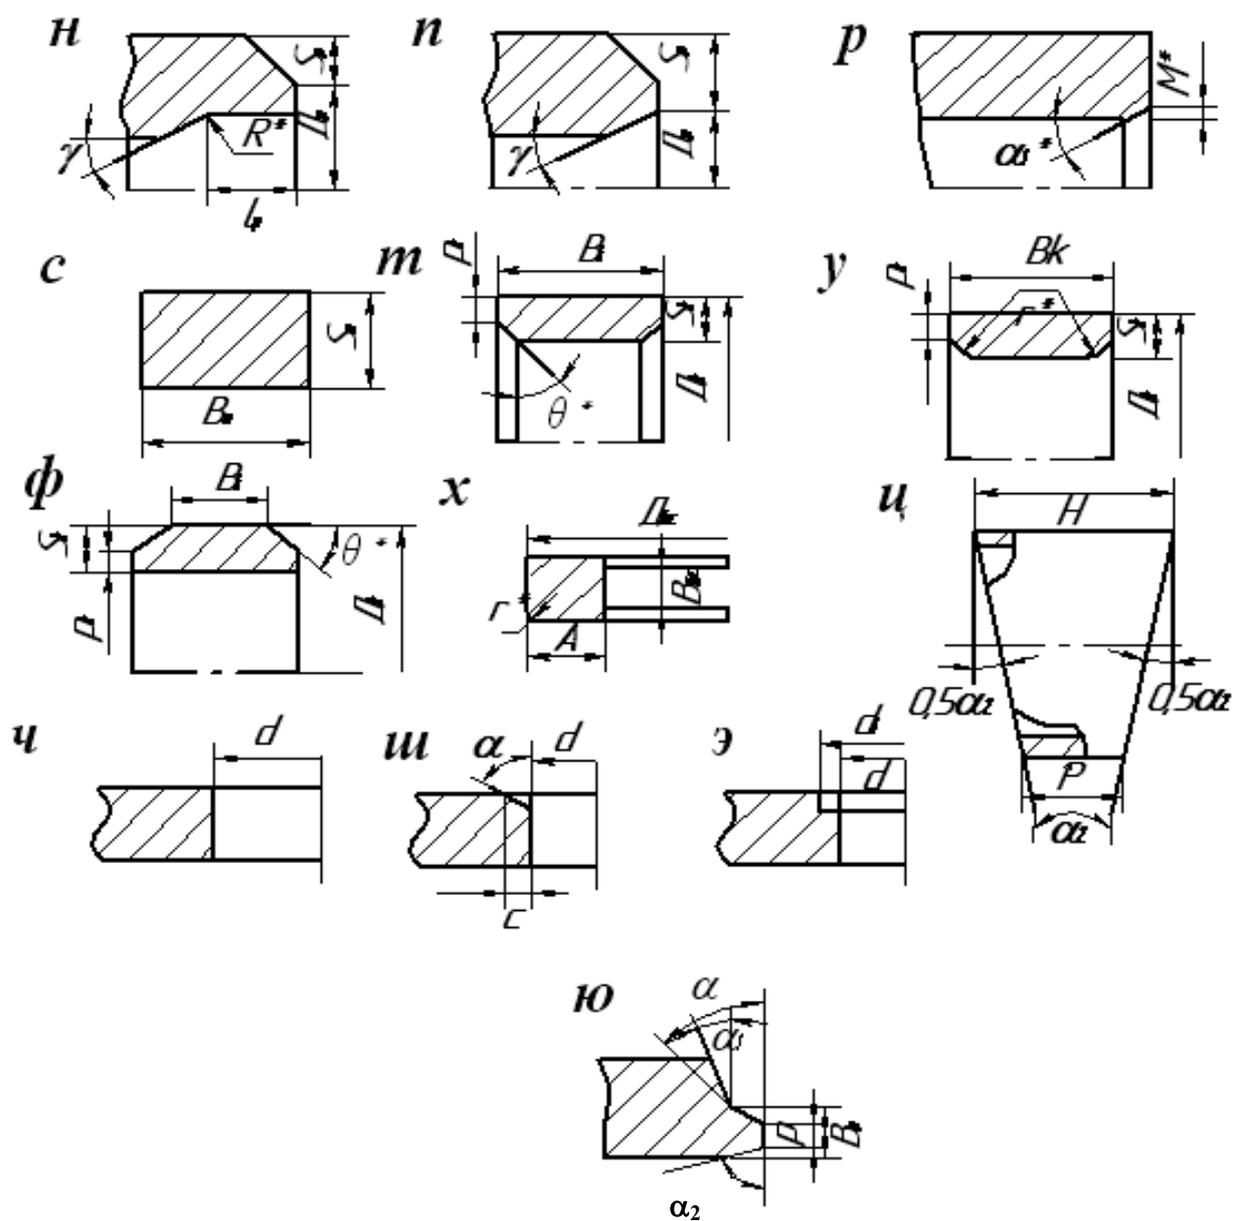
Продолжение. Размеры, контролируемые измерением при подготовке деталей под сварку (продолжение): *н* – цилиндрическая расточка (раздача) концов труб по внутреннему диаметру; *п* – коническая расточка труб по внутреннему диаметру; *р* – притупление внутренней кромки трубы; *с* – подкладная остающаяся пластина; *т, у* – подкладное стальное остающееся кольцо; *ф* – подкладное стальное остающееся кольцо; *х* – расплавляемая проволочная вставка; *ц* – сектор отвода; *ч, ш, э* – рассверловка отверстия под штуцер (патрубок) в корпусе (трубе, коллекторе); *ю* – разделка кромок под автоматическую сварку в среде защитных газов. *Примечание.* Размер измерению не подлежит, так как обеспечивается режущим инструментом и оценивается визуально
